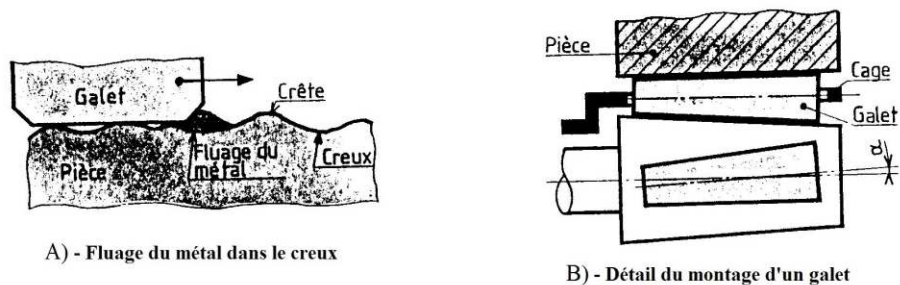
Finition des surfaces par galetage (brunissage)
